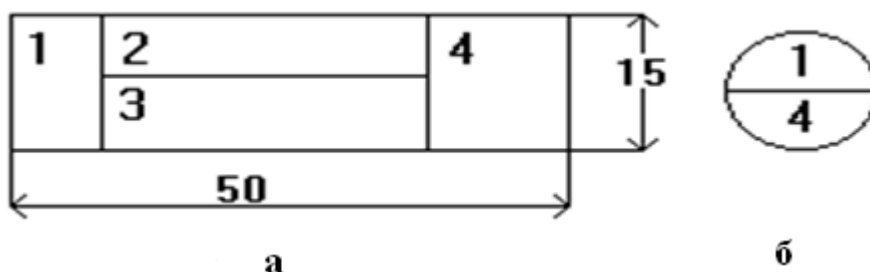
Условные обозначения деталей и сборочных единиц (а), крепежных деталей (б)
